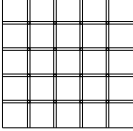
Kalıp yüzeyi drenaj kanal ve deliklerinin yerleşim planı
